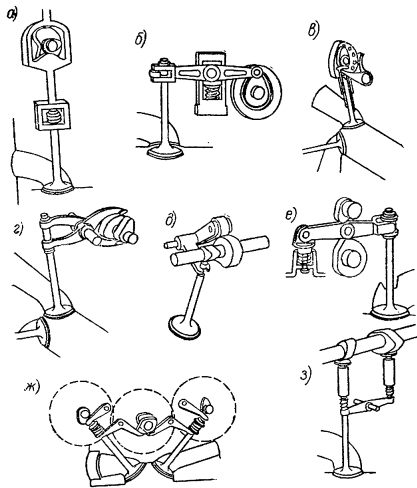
Конструктивные схемы десмодромического управления клапанами: а — фирмы «Делаж»; б — фирмы «Вагова»; в — фирмы «Мерседес-Бенц» для модели СЛР; г — фирмы «Мерседес-Бенц» для модели W-196; д — конструкции «Мазерати»; е — конструкции «Катанео»; ж — конструкции «Дукати»; з — инж. Стангуеллини
